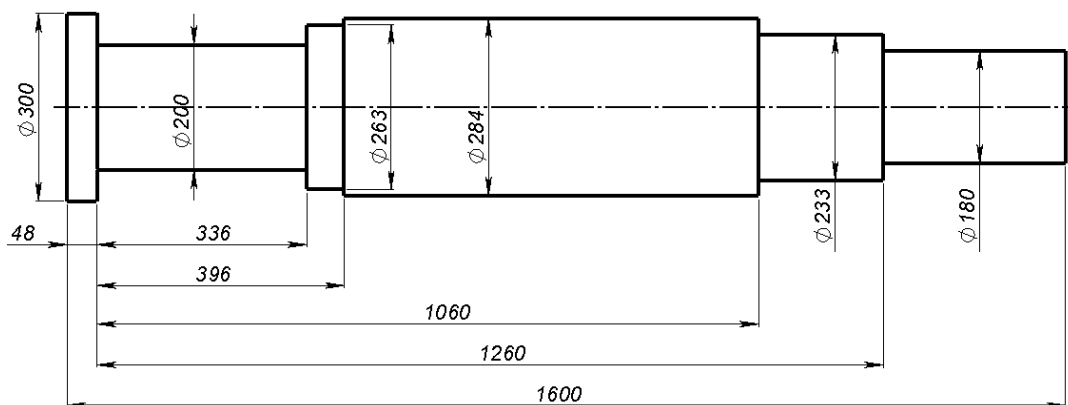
Розміри деталі (або обдраної заготовки)
